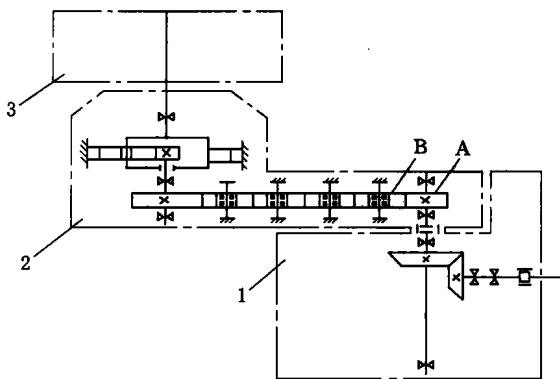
圆锥—圆柱齿轮—行星齿轮传动
